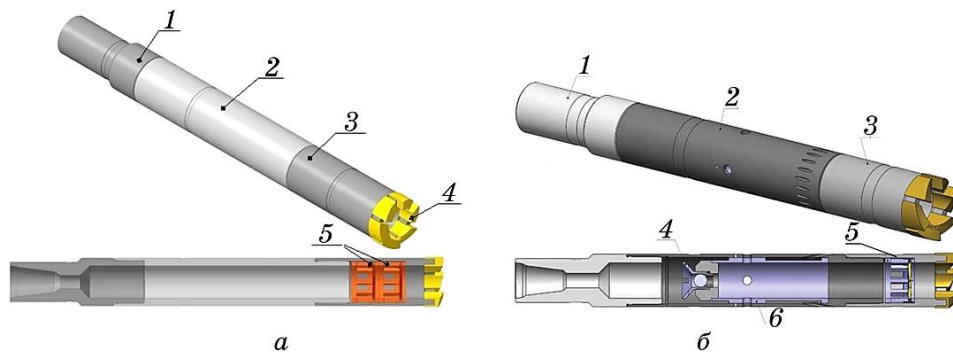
Павук: *a* — механічний (1 — перехідник, 2 — корпус, 3 — кільцева фреза, 4 — наварювання, 5 — уловлювач), *б* — гідравлічний (1 — перехідник, 2 — корпус, 3 — кільцева фреза, 4 — наварювання, 5 — кульовий хлипак, 6 — вкладень).
